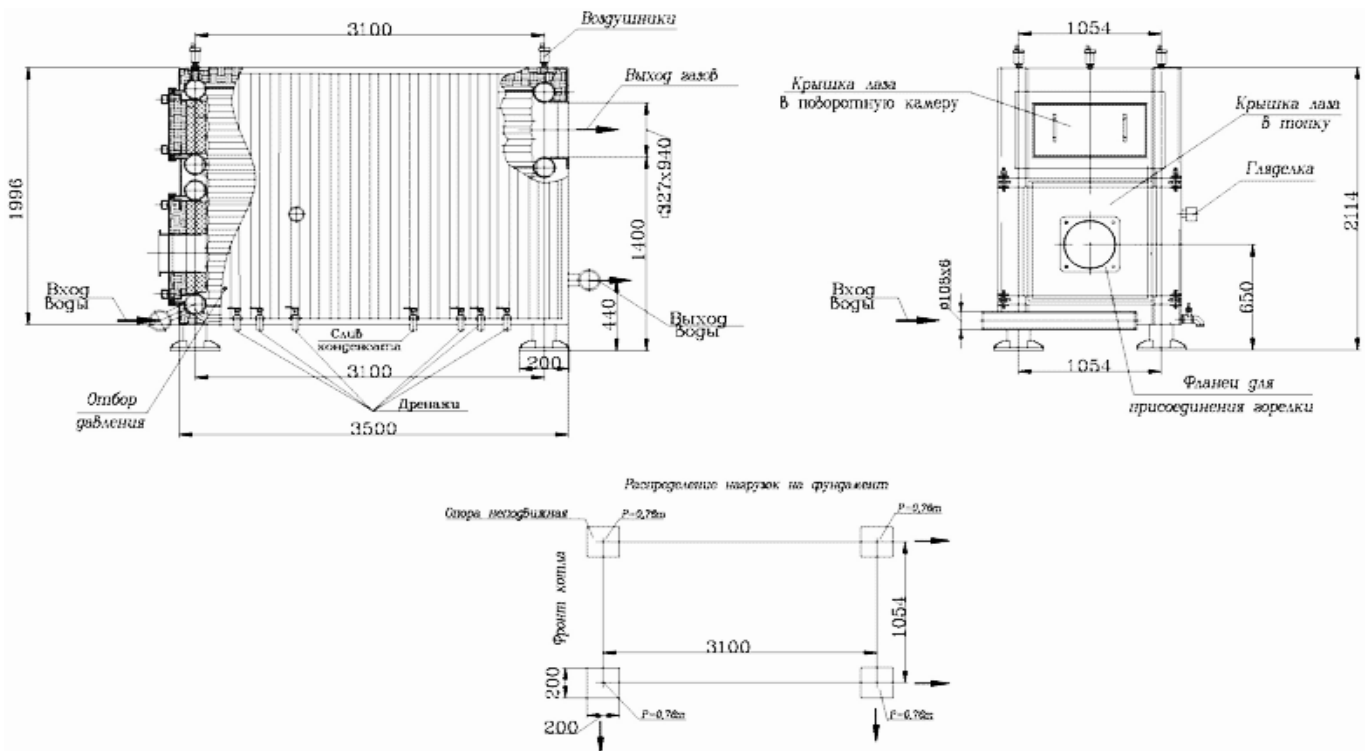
Устройство и габариты компоновки котла КВ-1,6
